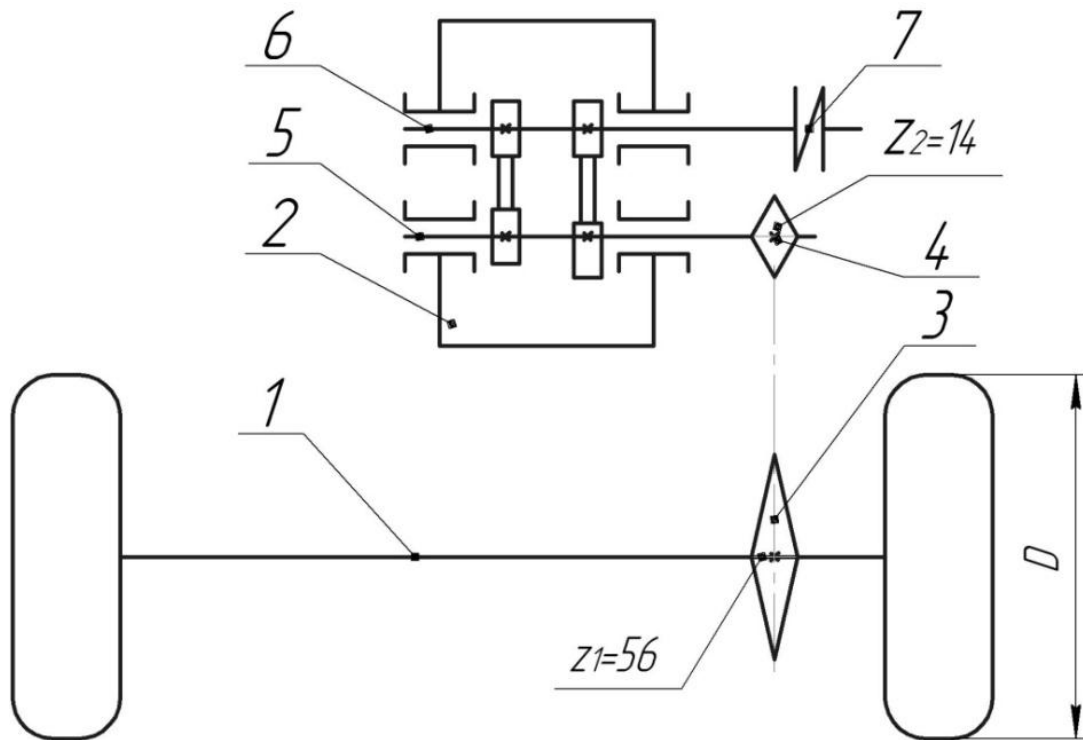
Кинематическая схема привода вала высаживающего аппарата сажалки лука-севка
